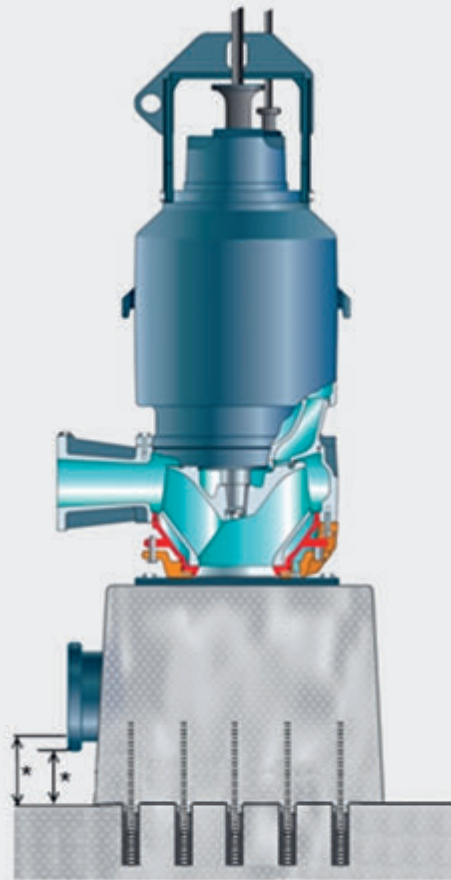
Вертикальный сухой монтаж погружного канализационного насоса Grundfos на бетонном фундаменте, соединенном фундаментными болтами с полом.
